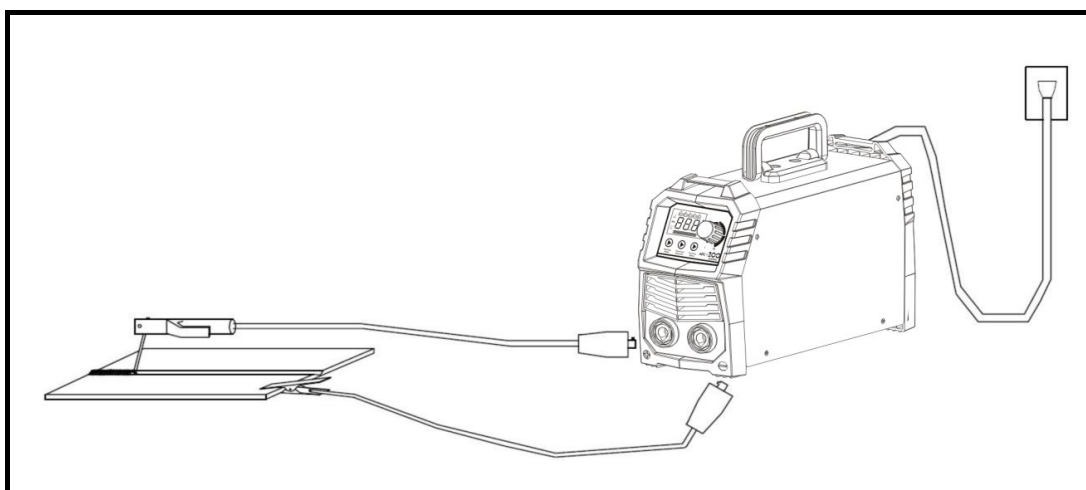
Schéma de la soudure MMA – Electrode enrobée
